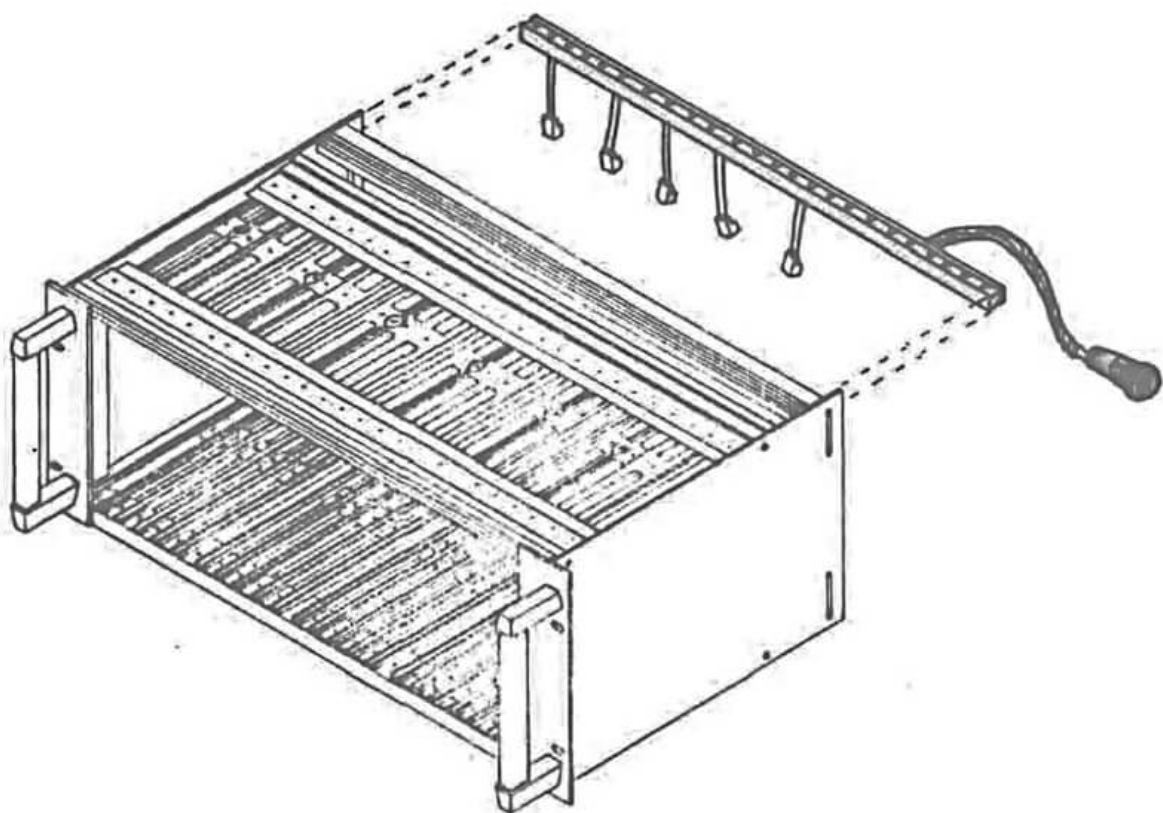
Estrutura SUB-5U-XX-1 - vista explodida
